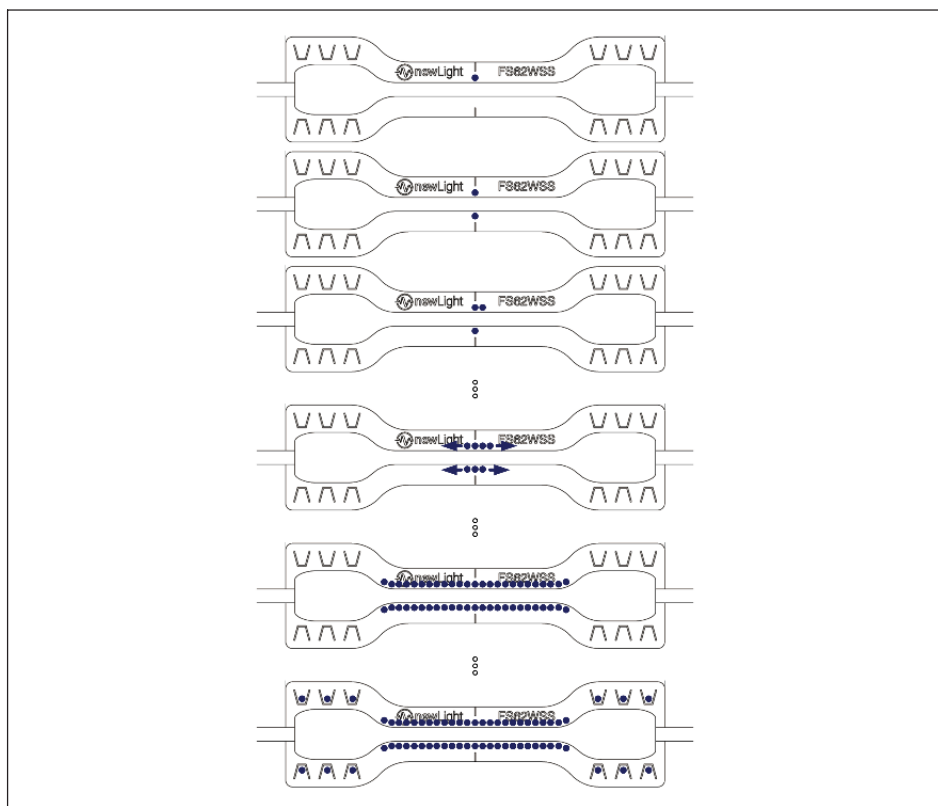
Procédure de soudage du FS62WSS
